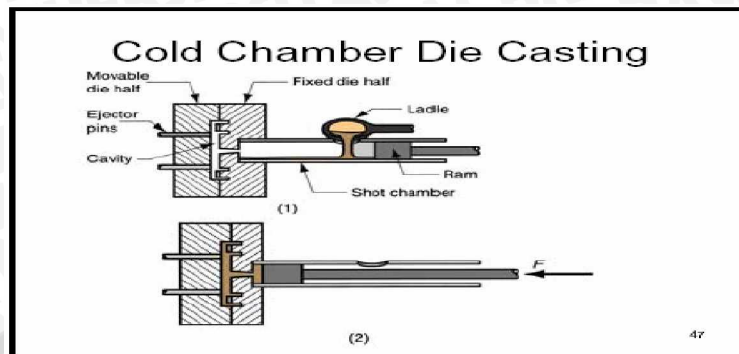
Ilustrasi skematis dari *Die Casting Machine
